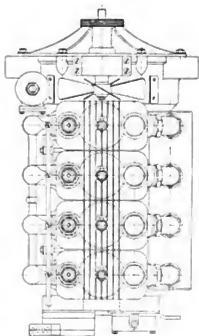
Dürkopp - Vierzylindermotor, Ansicht von oben.
